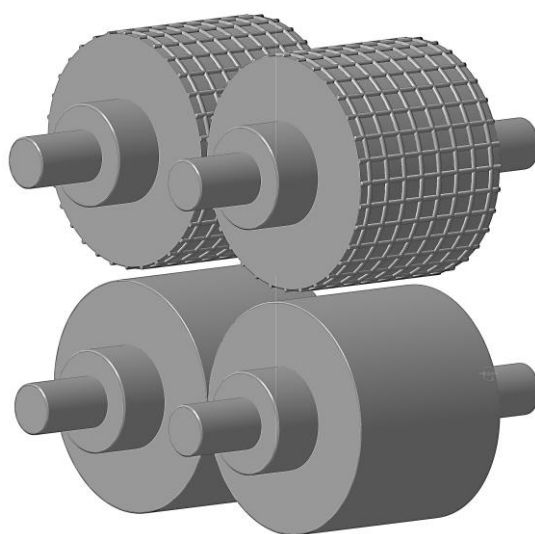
Схема четырехвалковой дробилки с использованием верхних валков с рифленой поверхностью бандажей
